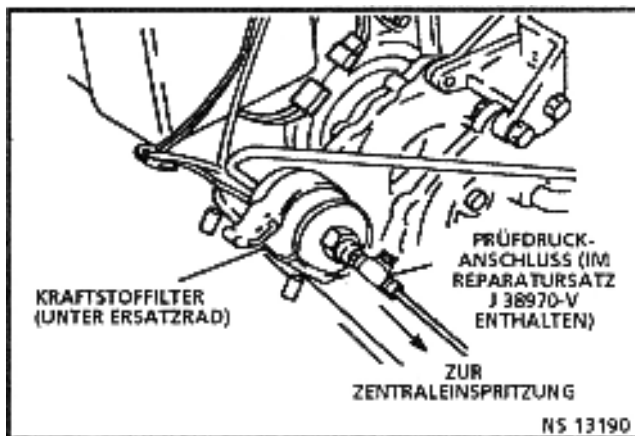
Einbaulage Prüfdruckanschluß
